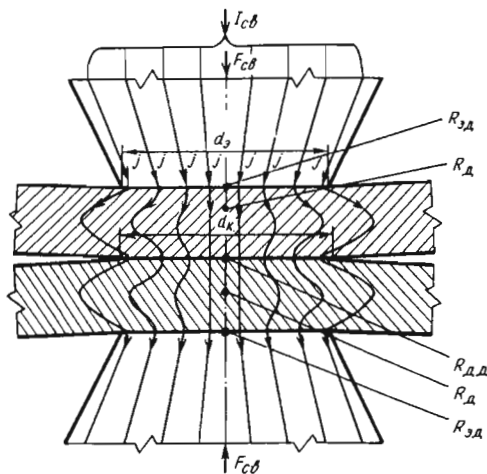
Схема сопротивлений и растекание тока в деталях при точечной сварке:
